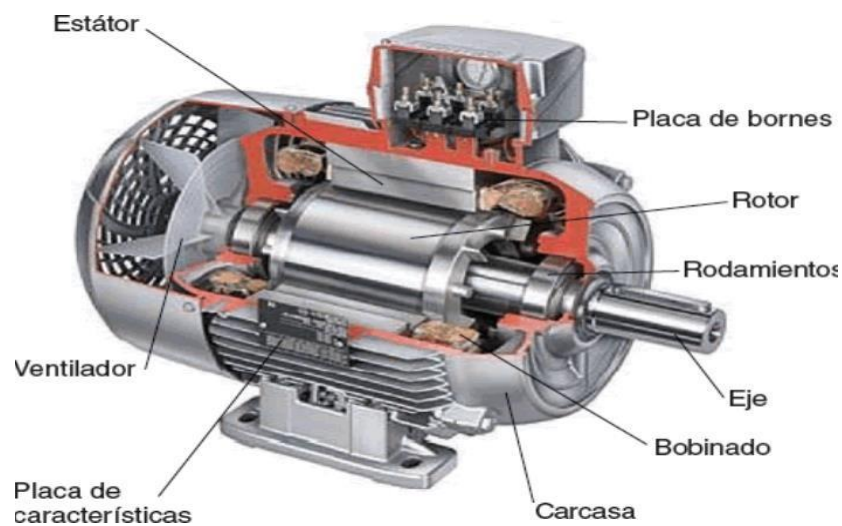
Partes de motor trifásico AC rotor jaula de ardilla.
